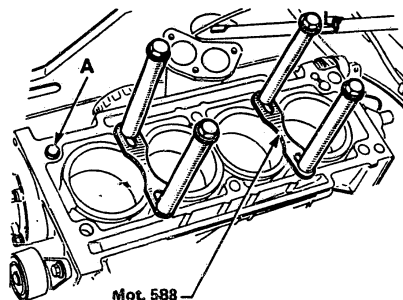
Der Motor darf ohne Zylinderkopf nur durchgedreht werden, wenn die Laufbüchsen auf ihren Sitz gespannt sind. A=Führungshülse, Mot. 988=Spezialwerkzeug.
